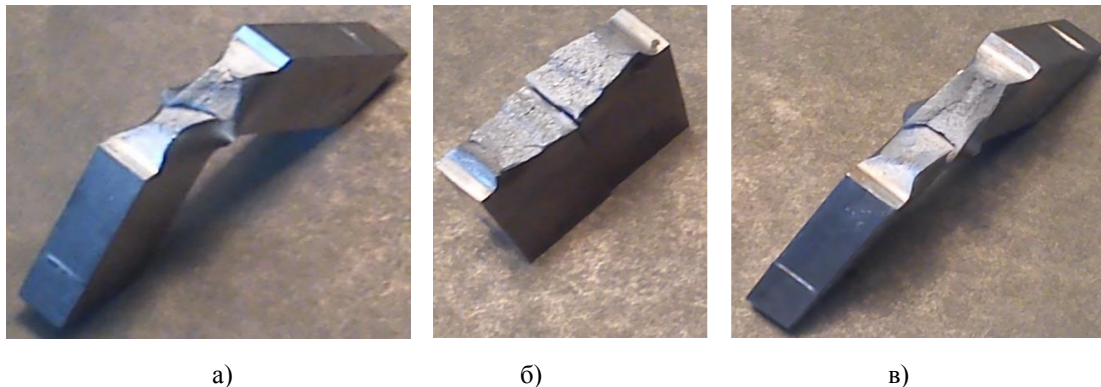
Общий вид разрушенных при 233 К образцов Менаже из стали 09Г2С с надрезом: а - в основном металле; б - в ЗТВ после РКУП; в - в ЗТВ после закалки и РКУП образцов с К-образным сварным швом
